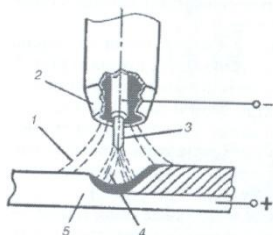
Схема дуговой сварки в атмосфере защитных газов:
